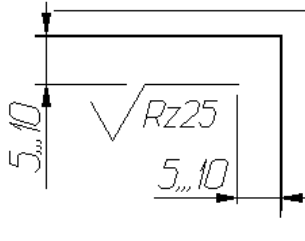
Указание шероховатости одинаковой для всех поверхностей изделия
